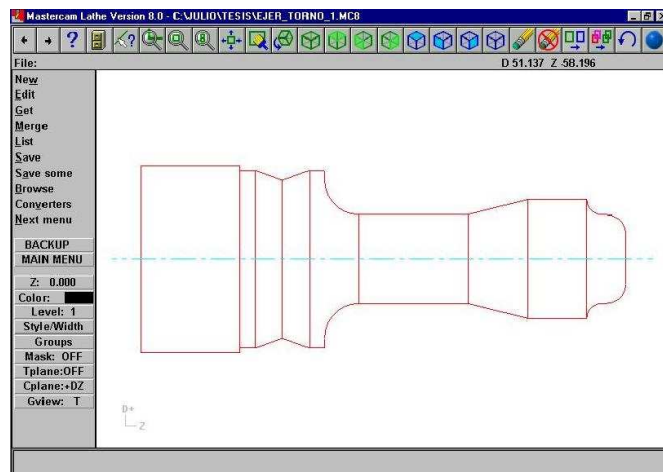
Pieza que debe ser maquinada mediante afine
